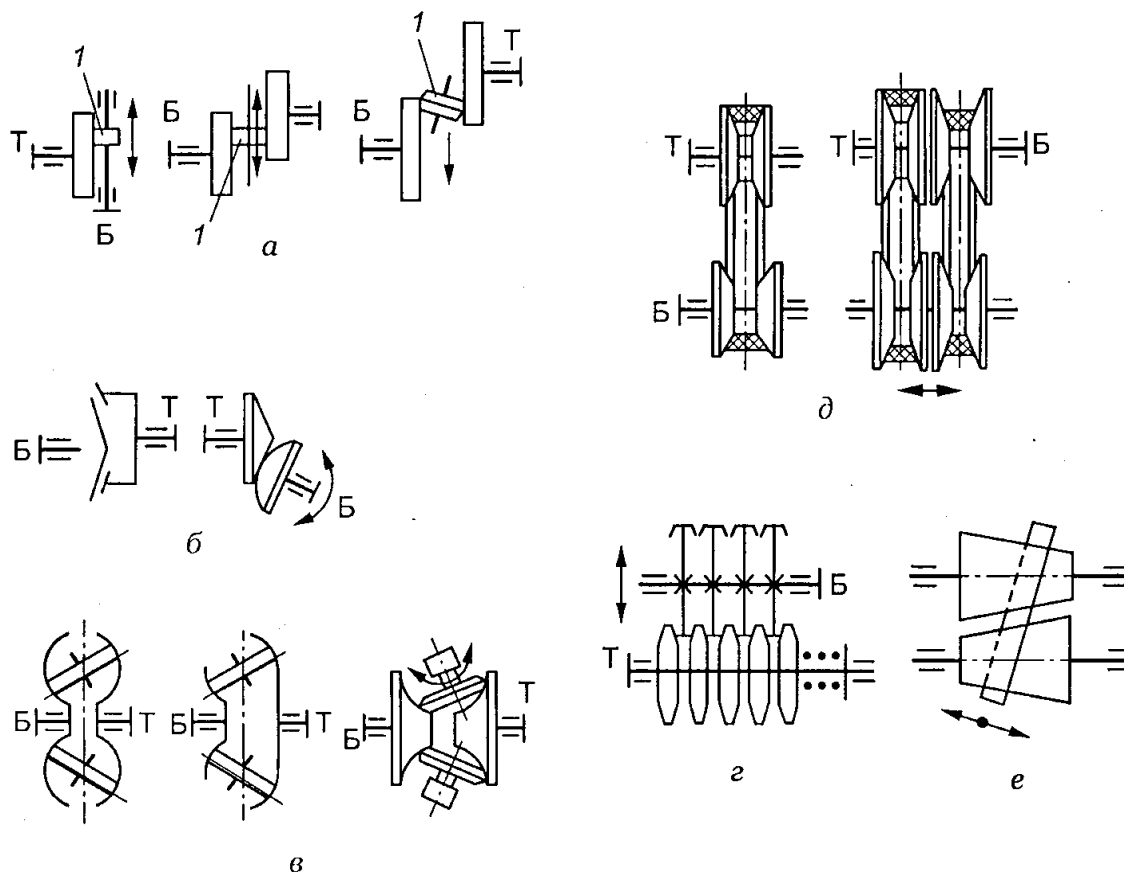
Схемы основных типов фрикционных вариаторов: а — лобовые; б — конусные; в — торовые; г — дисковый; д — клиноременные; е — двухконусный; 1 — ролик; Б — быстроходный вал; Т — тихоходный вал
